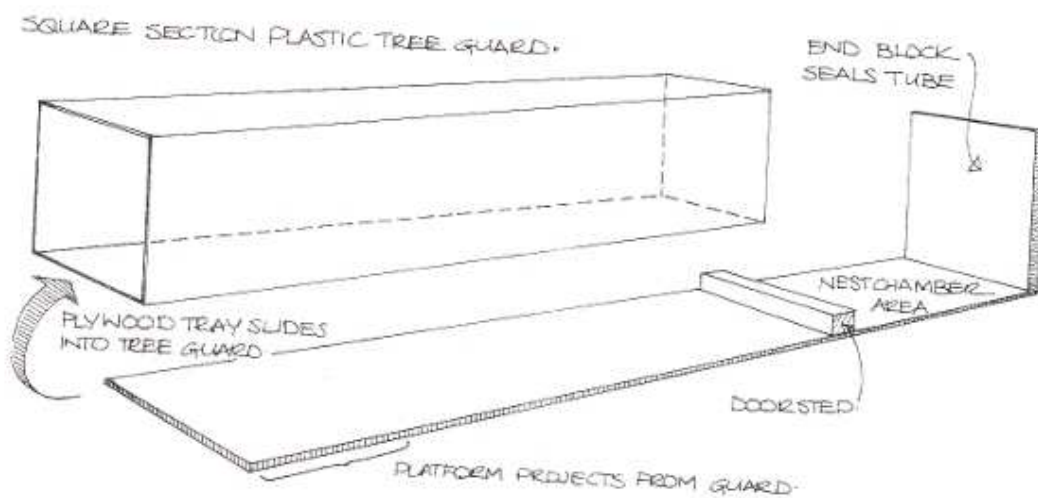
Plan de construction d'un nichoir en tube (d'après Morris) et installation dans les arbres.
